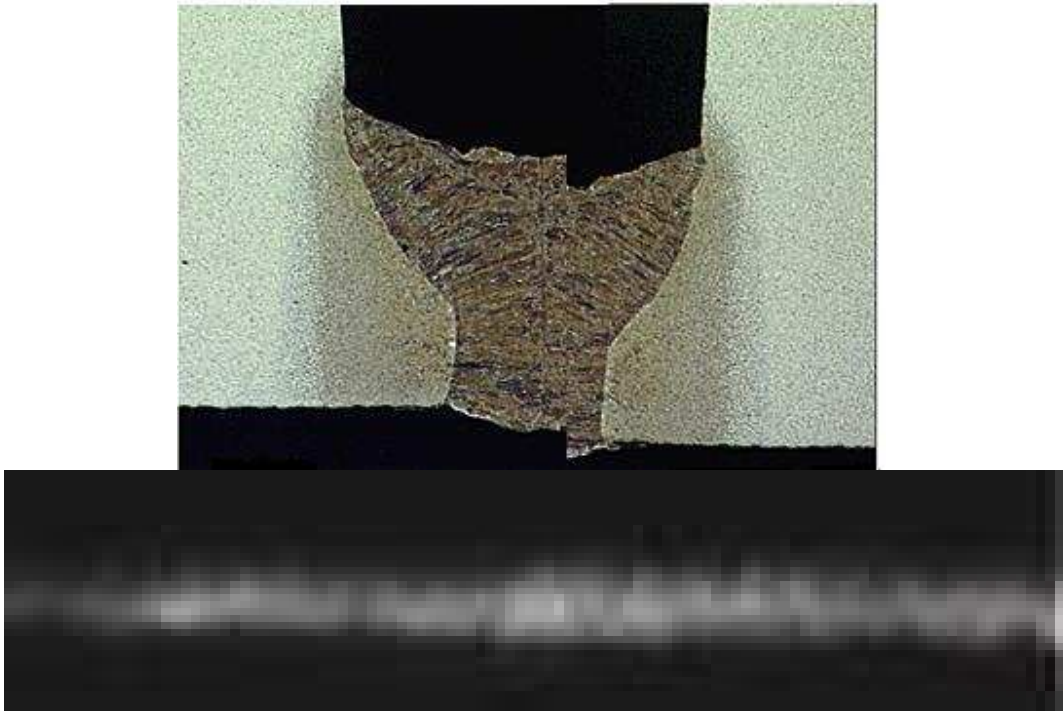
47 *Imagen radiográfica de Desalineamiento en la junta soldada.
